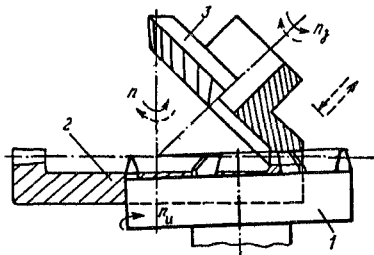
Схема нарезания круговых зубьев конических колес (n_1 — частота вращения резцовой головки)
